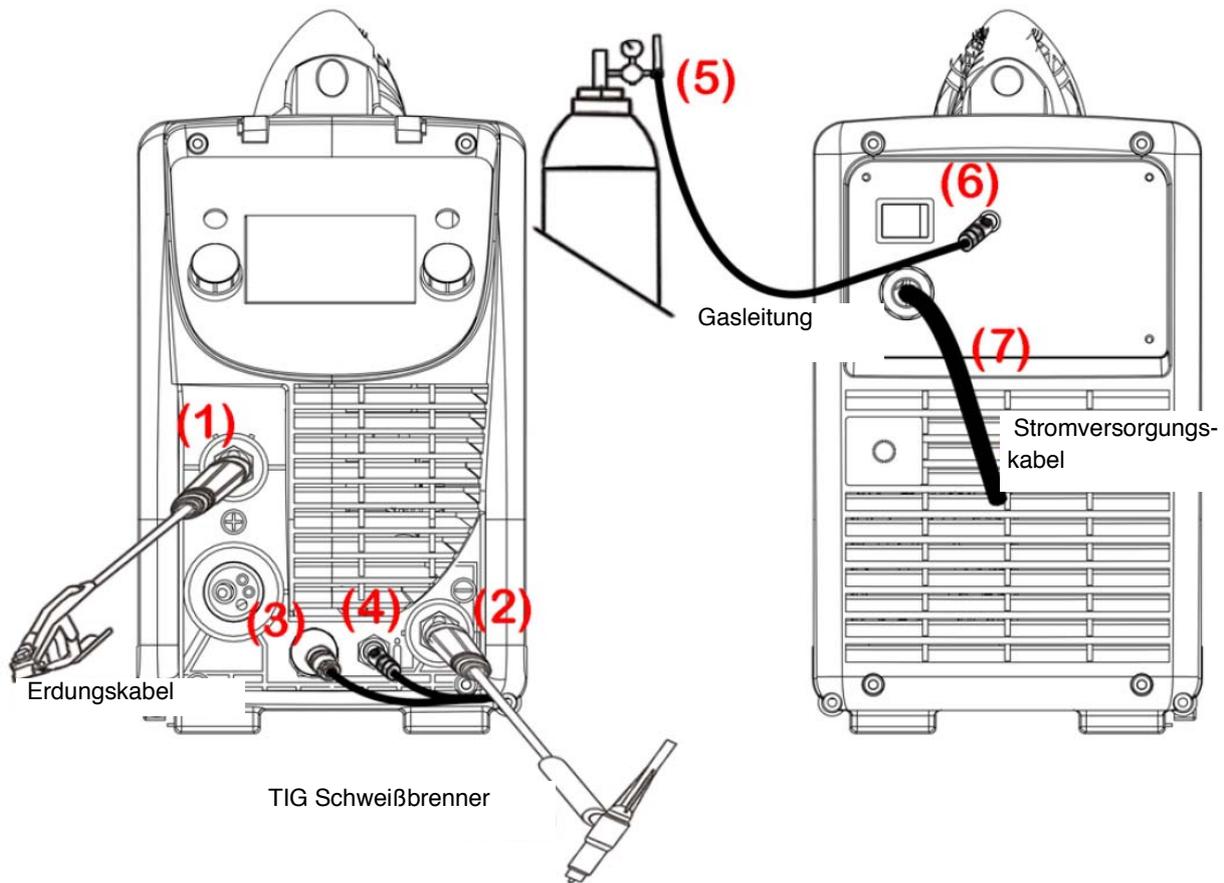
Aufbau TIG-Schweißverfahren
